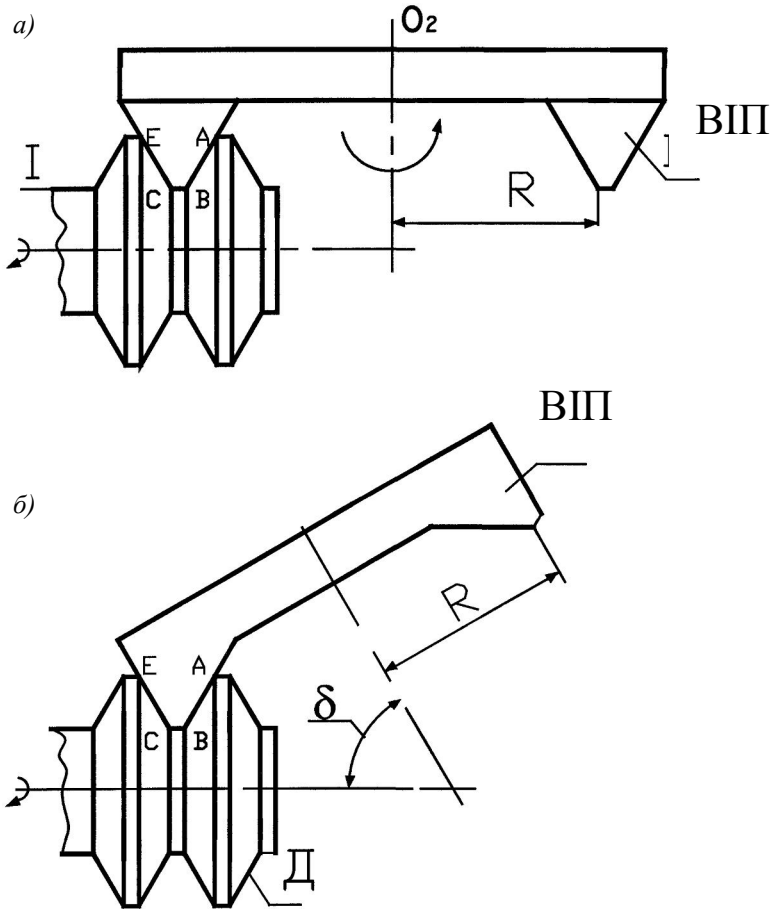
Оброблення торцевими фрезами деталей типу «шків»
